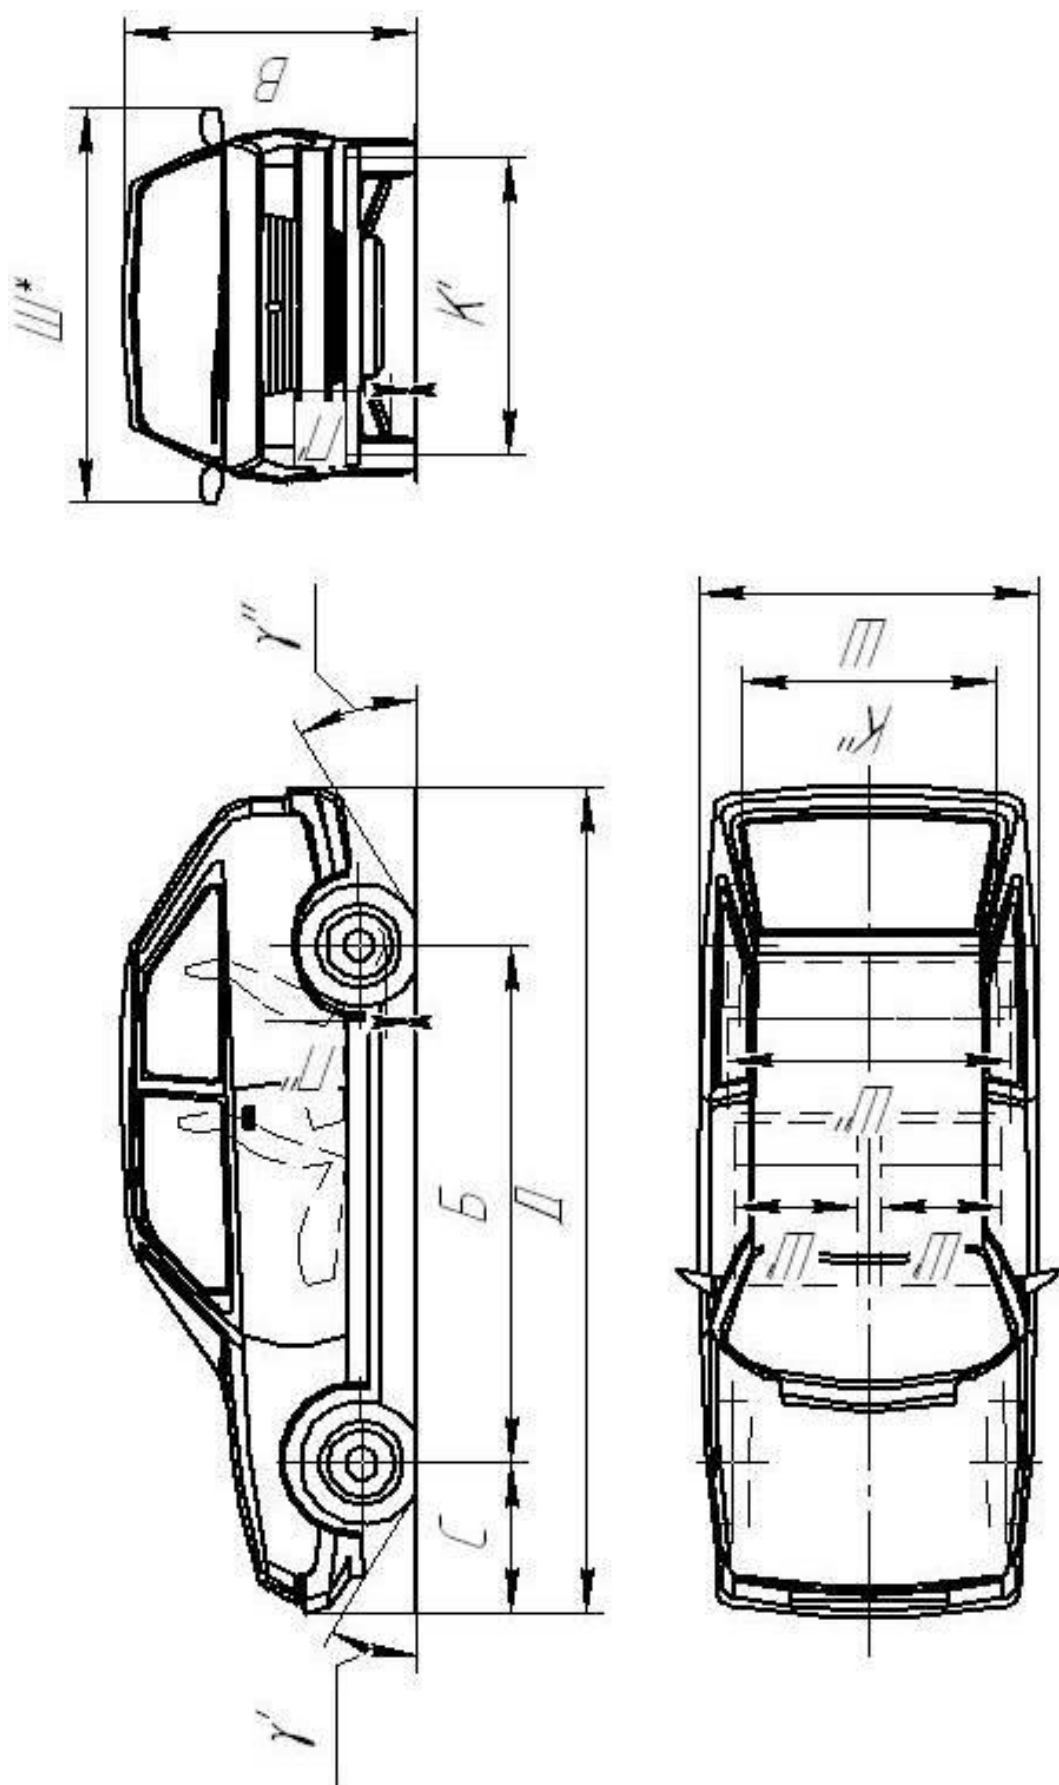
Размерные параметры легкового автомобиля ЗАЗ-1102
